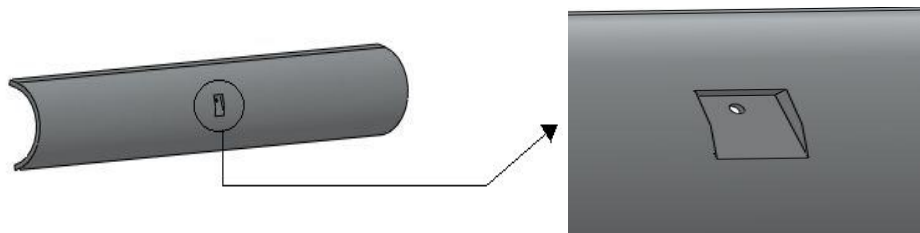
C-FORMET BOM SOM IKKE KREVER SVEISING
